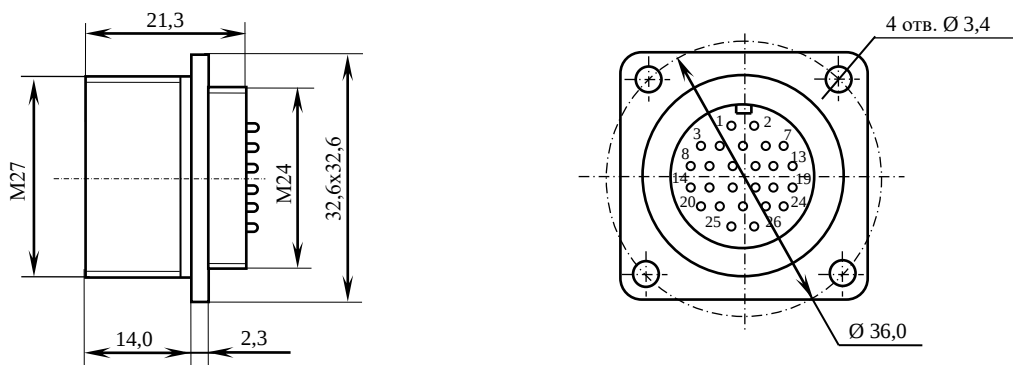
Габаритные и установочные размеры блочной розетки
